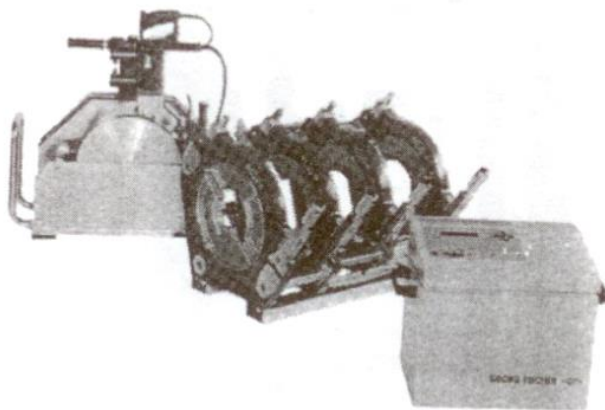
Сварочные машины GF 160-CNC, GF 315-CNC, GF 500-CNC и GF 630-CNC фирмы «GEORG FISCHER»
